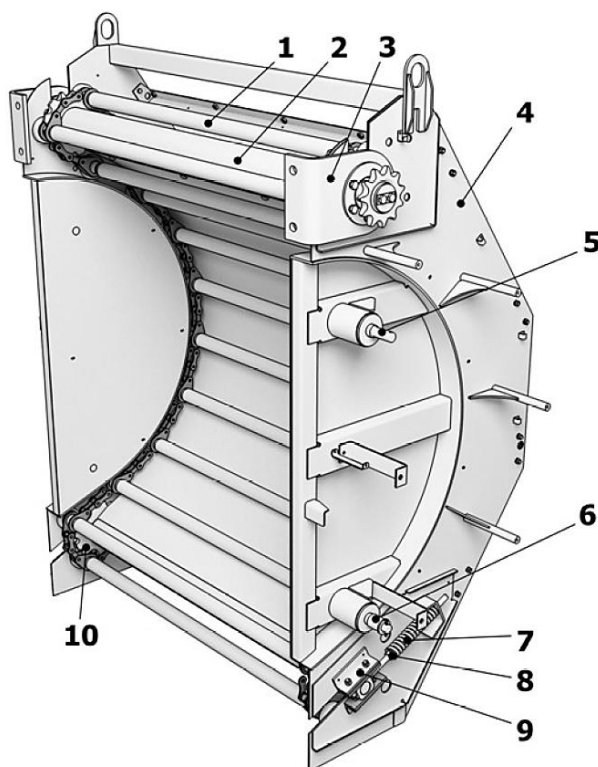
Камера задняя: 1 – цепочно-планчатый механизм; 2 – ведущий вал; 3 – опорный кронштейн; 4 – рама; 5 – ось гидроцилиндра; 6 – ось механизма фиксации; 7 – пружина; 8 – гайка; 9 – направляющая; 10 – ведомый вал
